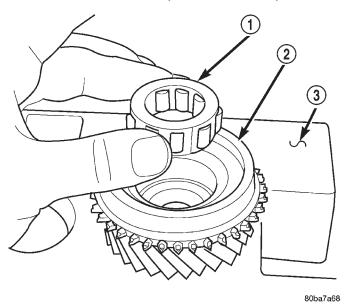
EJE IMPULSOR Y COJINETE DE GUIA
